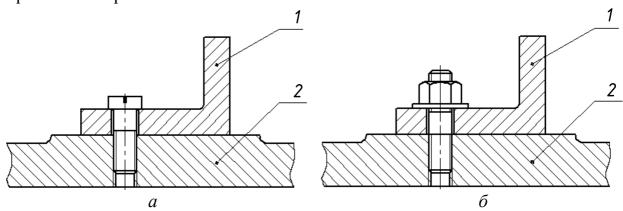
Резьбовое соединение с применением: а) винта; б) шпильки, гайки и шайбы
